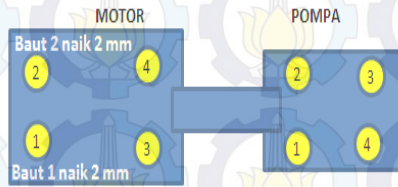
Posisi baut pada prototype base pompa dan motor
